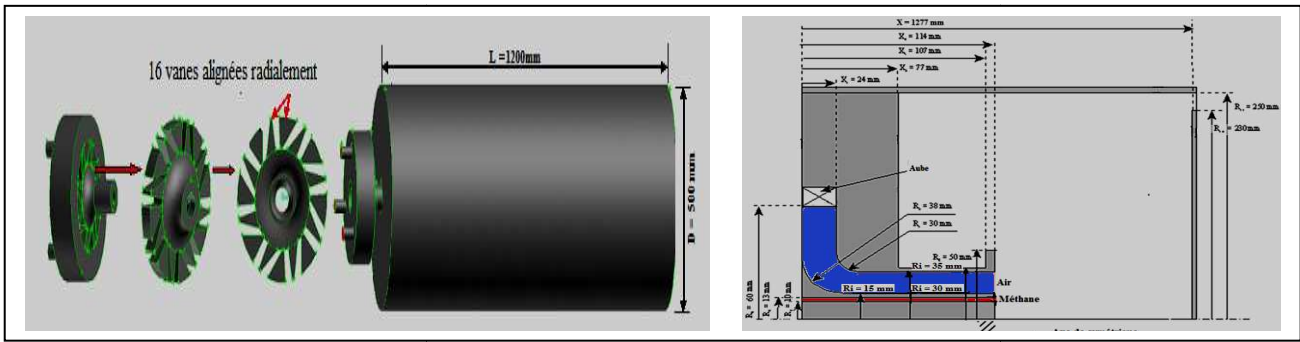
Géométrie du brûleur et de la chambre de combustion
